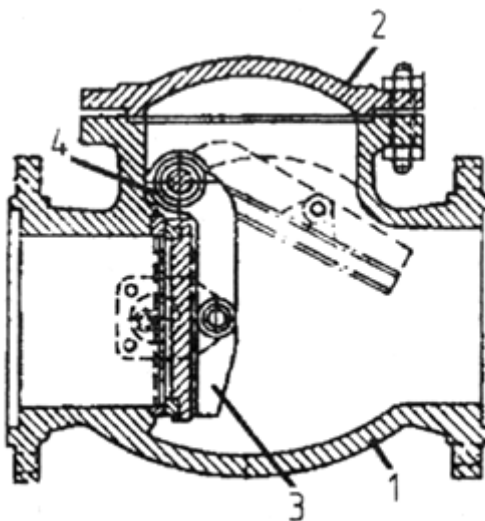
Поворотный обратный клапан D_y 50 - 600 мм
